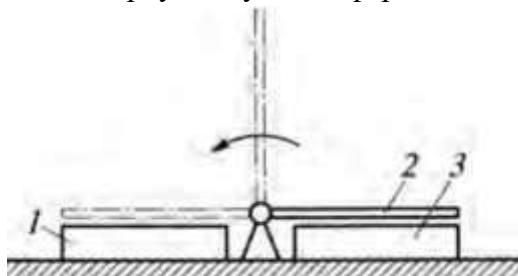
Схема устройства для сборки и сварки ферм
